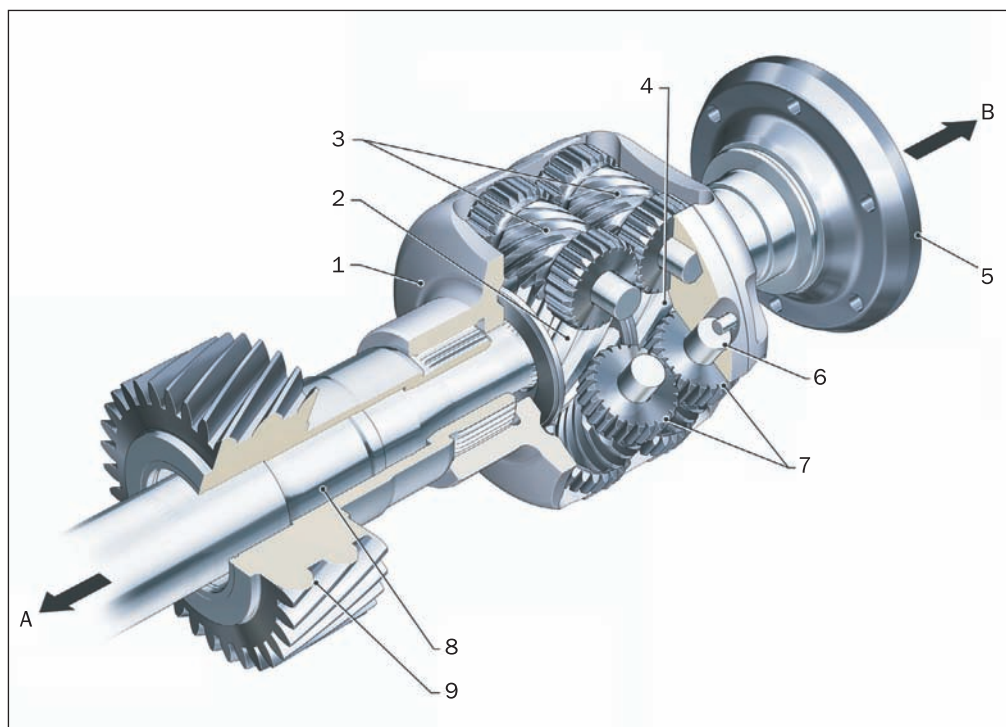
Межосевой дифференциал Torsen автомобиля Audi Quattro: 1 — корпус дифференциала; 2,4 — передняя и задняя шестерни; 3 — червячные сателлиты; 5 — фланец карданной передачи; 6 — ось сателлитов; 7 — прямозубые шестерни; 8 — ведомый вал; 9 — полый ведущий вал; А — к передней оси; В — к задней оси
